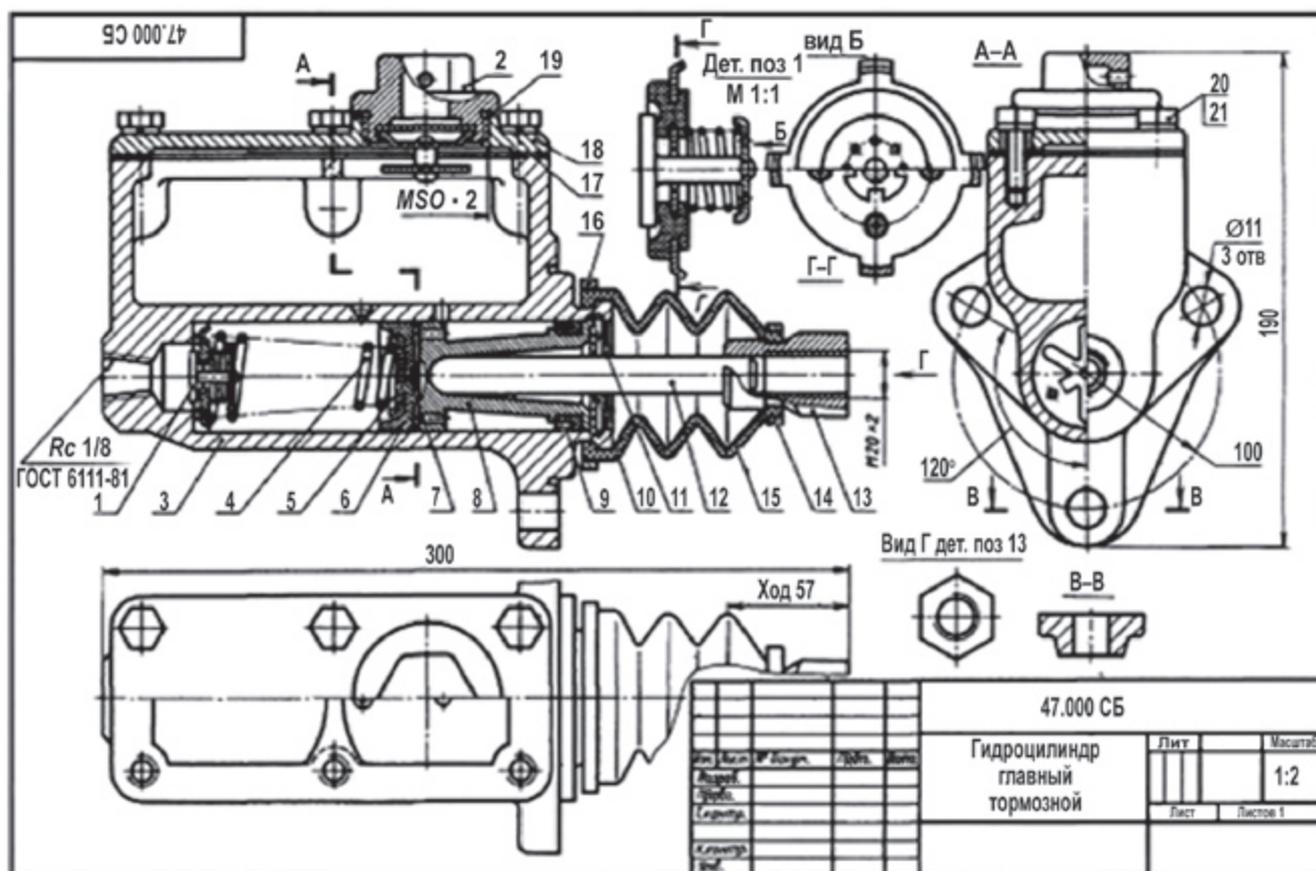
Сборочный чертеж гидроцилиндра главного тормозного. Чертеж № 47.000 СБ
